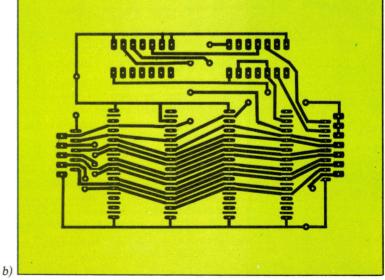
Le circuit imprimé côté « soudures ».
